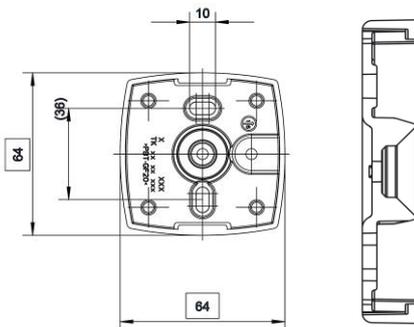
Vista desde arriba y sección de la placa adaptadora
